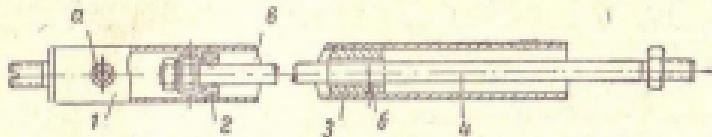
Гидравлический амортизатор передней вилки мотоцикла М-72.
